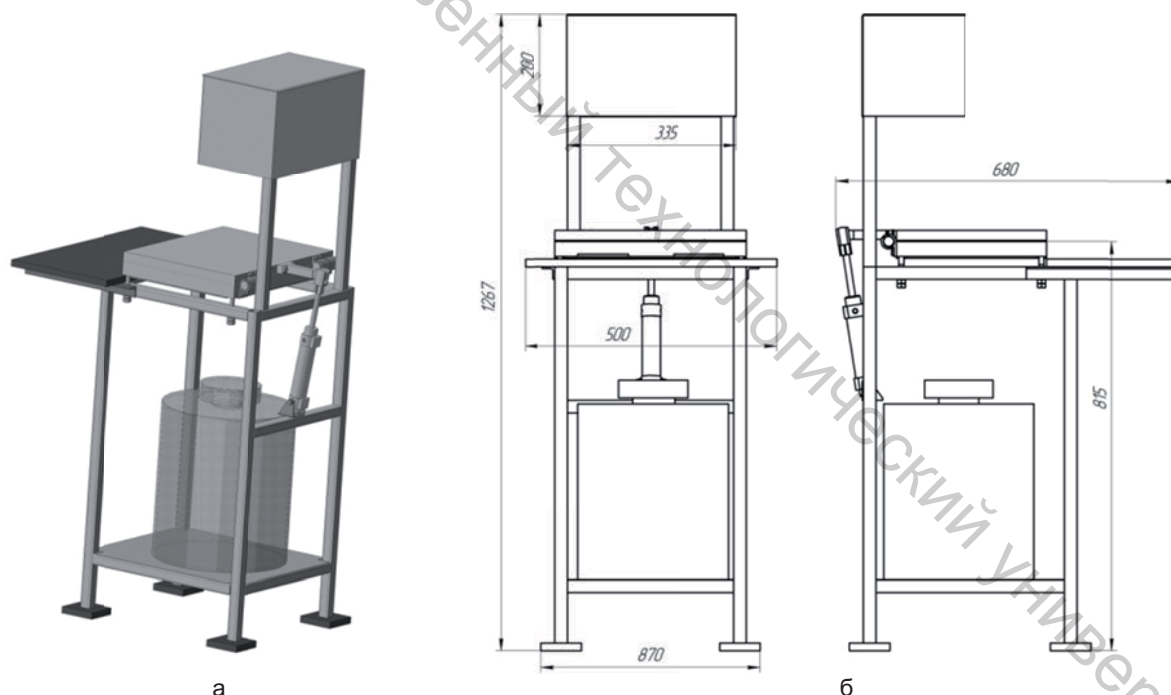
Общий паровлажнителя союзок «ПУ-Белвест»: а) 3D-модель общего вида; б) габаритные размеры паровлажнителя
